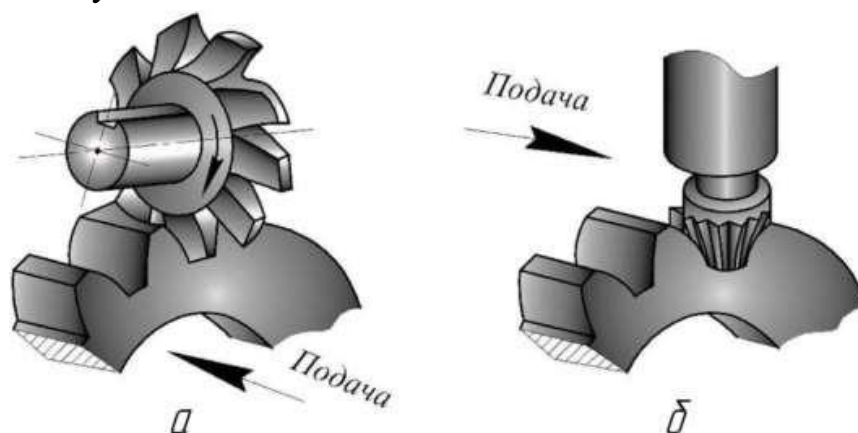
Нарізування зубців методом копіювання: а – дисковою фрезою; б – пальцевою фрезою
